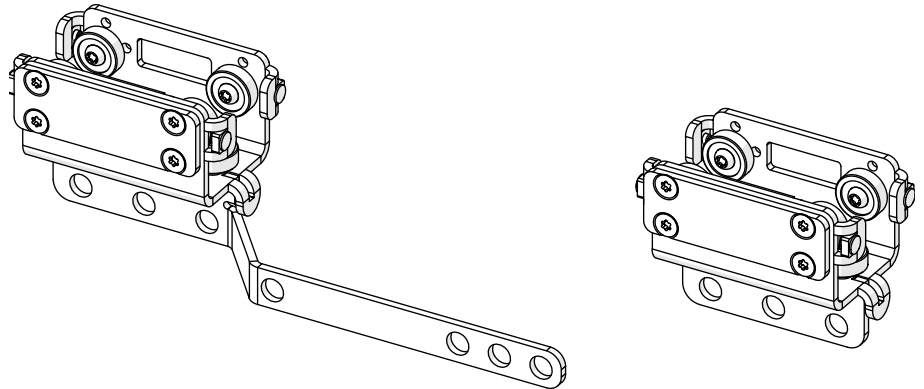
Zugwagen mit Riemenklemme sowie rechtsseitigem Überzugbügel (links) und Zugwagen mit Riemenklemme (rechts)
